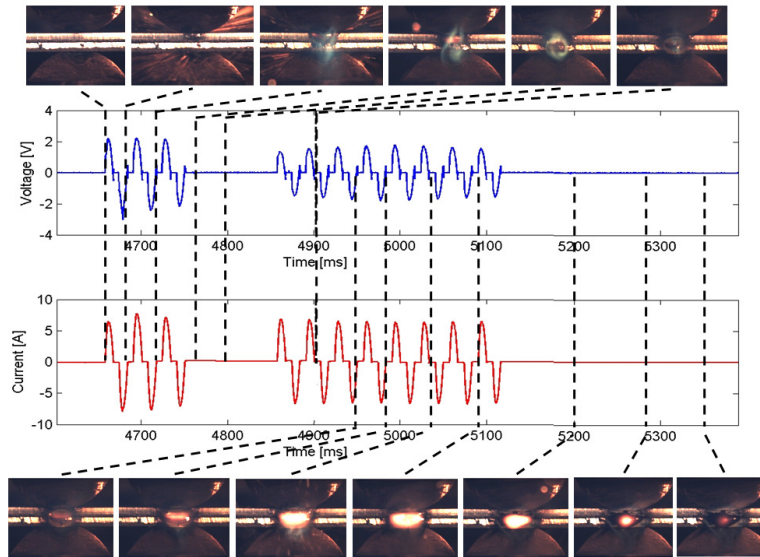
Filmagem do processo de soldagem com a técnica de “burn-zinc”
